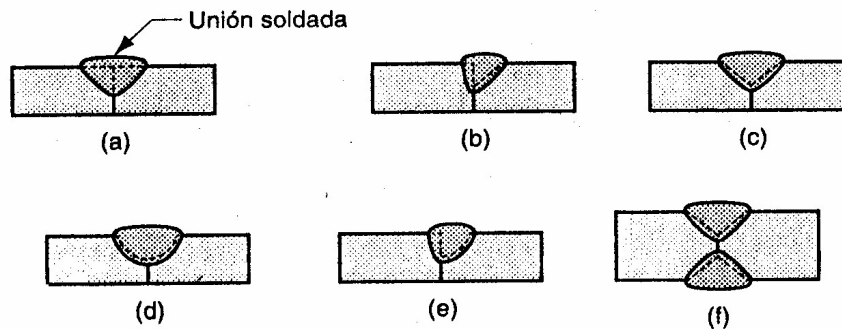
Algunas soldaduras con bisel típicas: a) soldadura con bisel cuadrado en un lado; b) soldadura con bisel único; c) soldadura con bisel en V único; d) soldadura con bisel en U único; e) soldadura con bisel en J único; f) soldadura con surco en X para secciones más gruesas. Las líneas con guiones muestran los bordes originales de las partes.
